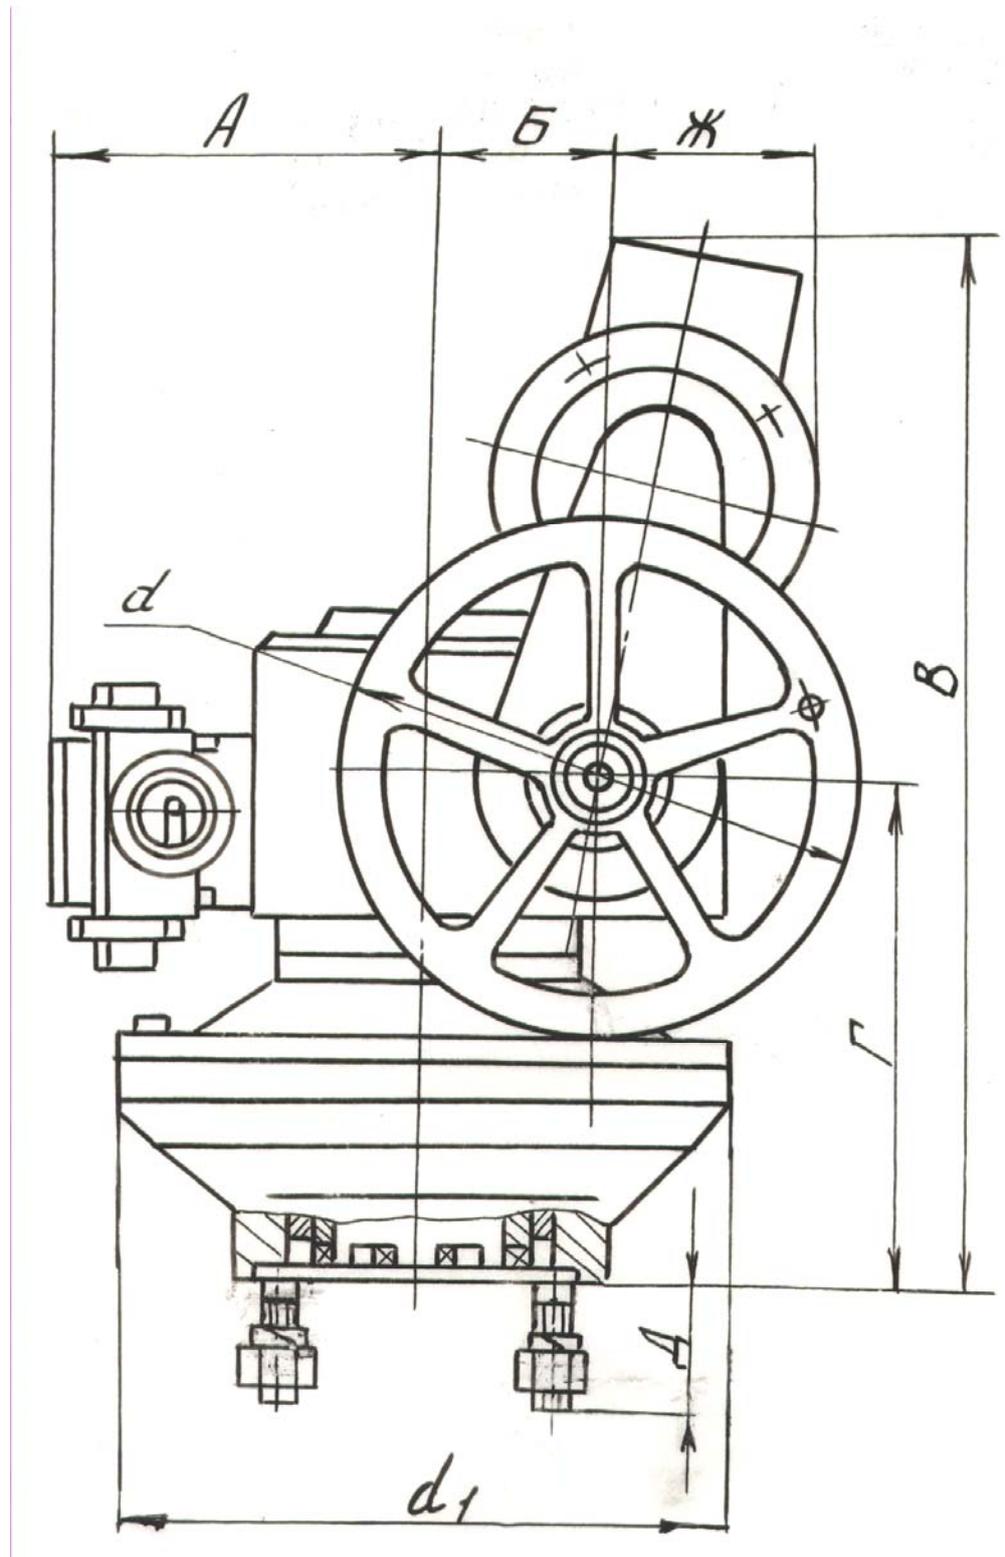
Общий вид и габаритные размеры электропривода типа Д
